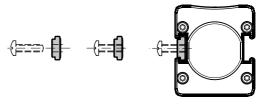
MONTAGE MIT BEFESTIGUNGSMUTTER UND M5-SCHRAUBE
